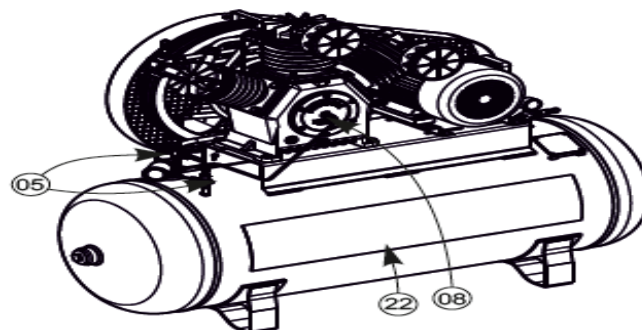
Partes que componen un Compresor Alternativo Lubricado
